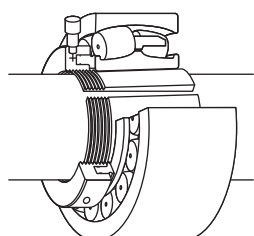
Piuliță hidraulică folosită la montarea rulmentului pe o bucă de strângere.
